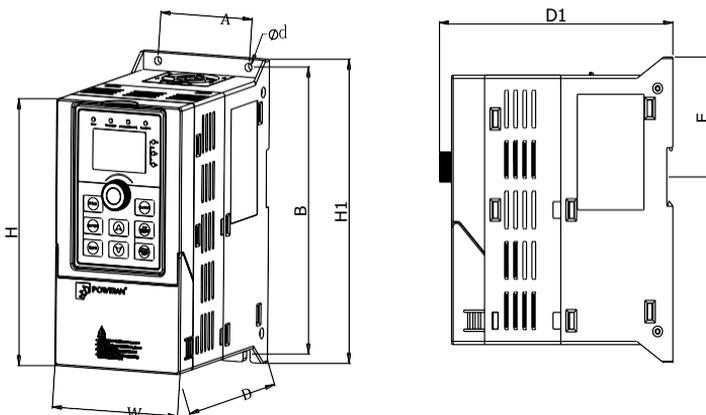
15kW G3 desenho externo do produto, dimensional instalação
